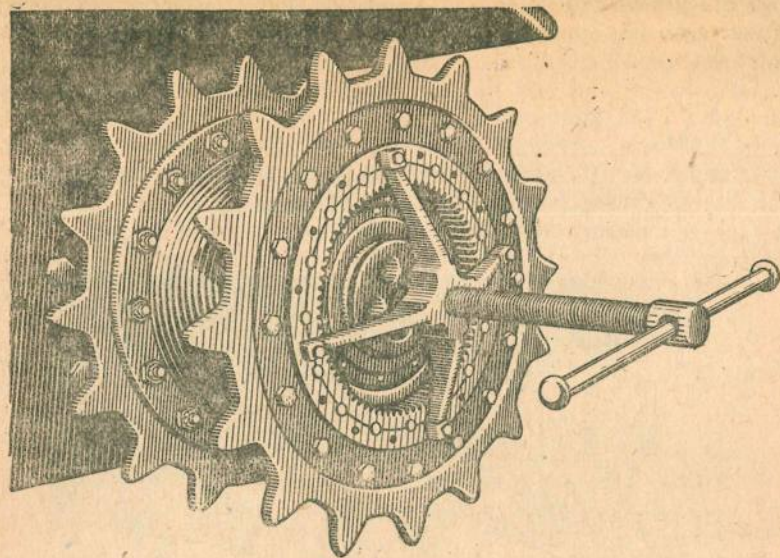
Снятие ведущего колеса с кронштейна при помощи приспособления № 3916
